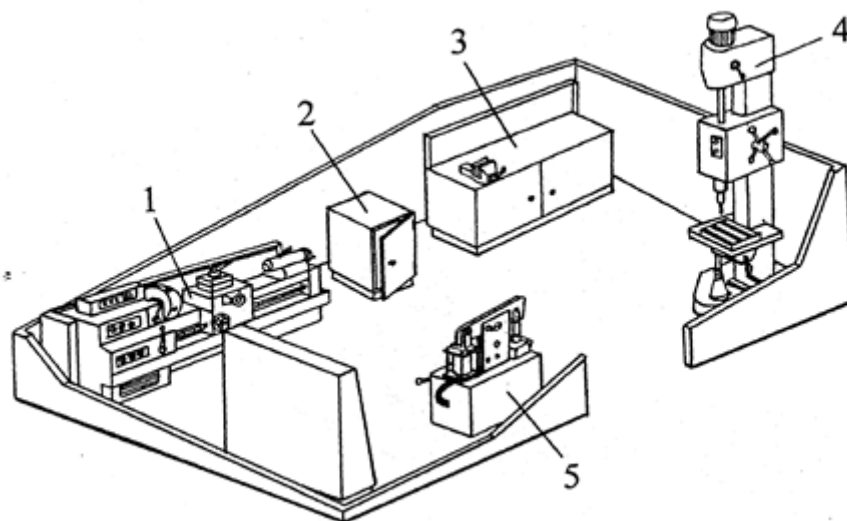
Слюсарно-механічна дільниця : 1 – універсальний токарно-гвинторізний верстат 1В62Г; 2 – тумбочка інструментальна ОРГ-1611; 3 – верстат слюсарний з настільним точильно-шліфувальним верстатом 3Е631; 4 – верстат радіально-свердлильний 2К52-1; 5 – універсальна установка для ремонтних робіт ОР-12561
